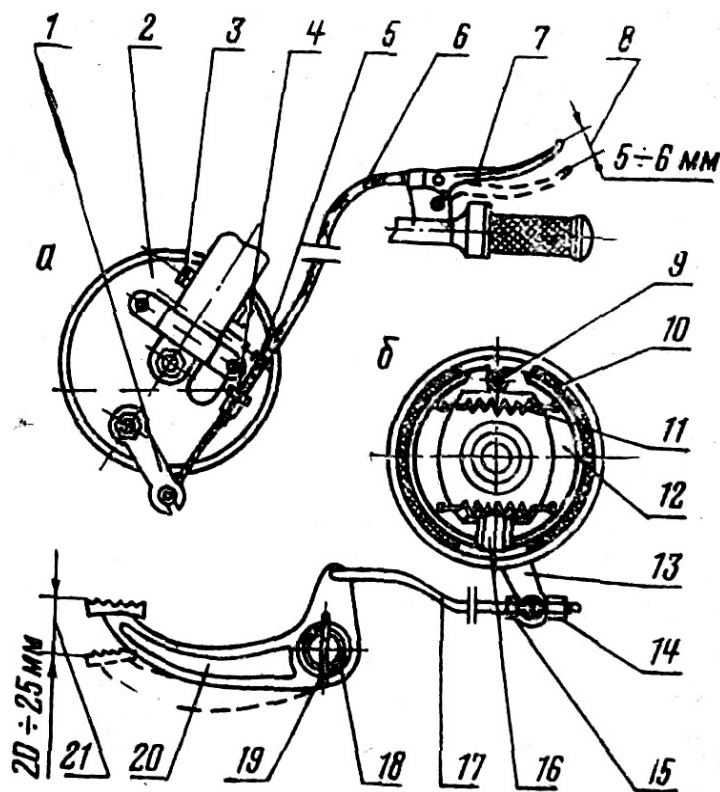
Тормоза: а — передний; б — задний; 1 и 13 — рычаг тормозного кулачка; 2 — тормозной диск; 3 — реактивный упор; 4 — контргайка; 5 — регулировочный винт; 6 — трос; 7 — рычаг переднего тормоза; 8 — свободный ход рычага; 9 — ось колодок; 10 — накладка 11 — пружина колодок; 12 — тормозная колодка; 14 — регулировочная гайка; 16 — контргайка; 16 — разжимной кулачок; 17 — тяга; 18 — втулка тормозной педали; 19 — штифт; 20 — тормозная педаль; 21 — свободный ход педали
